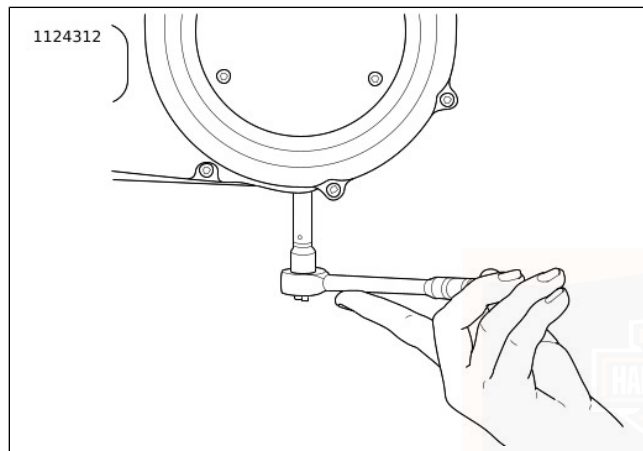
Ausbau/Einbau der Kettengehäuse-Ablassschraube
